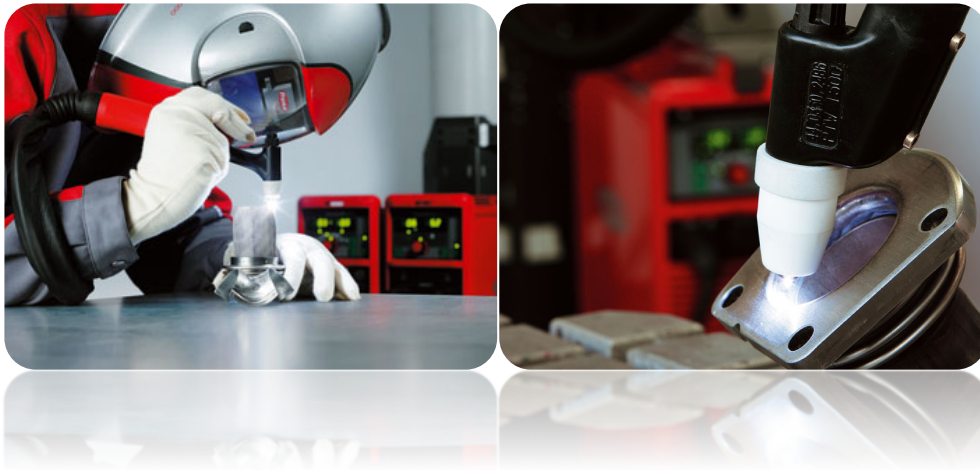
Exemple mètode de fusió, soldadura micro-plasma.
